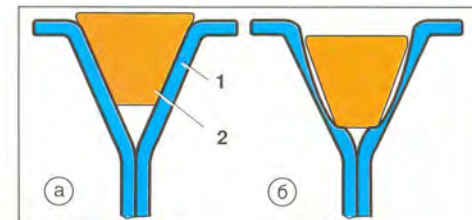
Профиль канавки в шкиве генератора: а – новая; б – изношенная; 1 – шкив; 2 – ремень.
